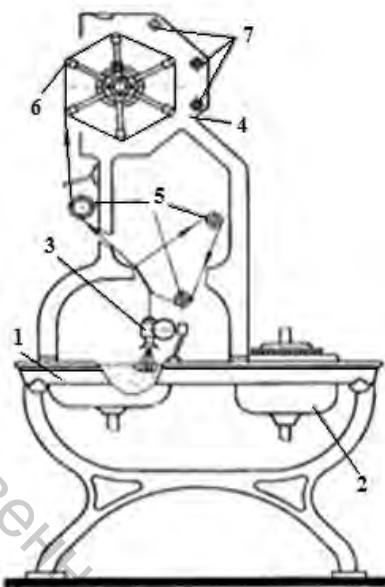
Шелкомотальный станок с верхним уборочным устройством КМС–10 ВУ: 1– станина, 2– запарочный котелок, 3– ловитель, 4– сушильный шкаф, 5–нитенаправляющие блочки, 6– мотовила, 7–паровые трубы
